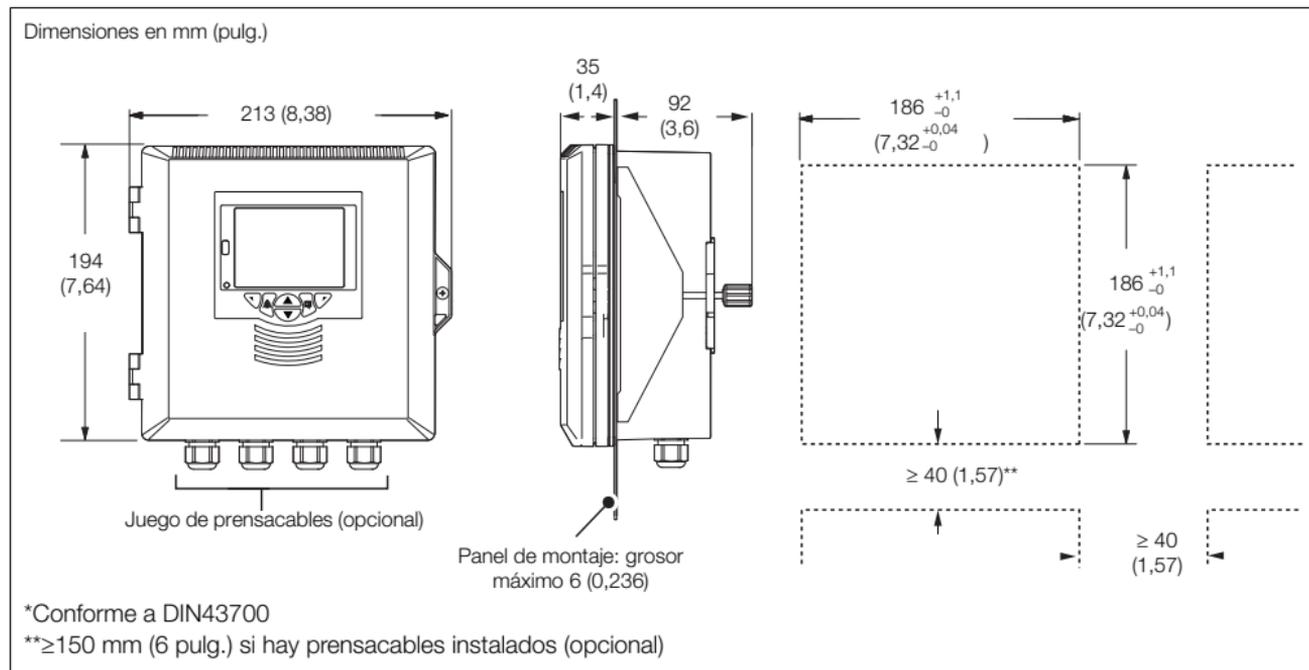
Opción de montaje en panel del ControlMaster CMF160
